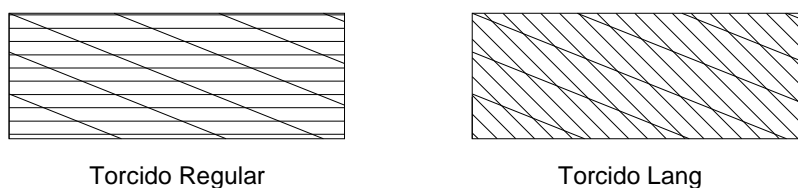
Tipos de fabricación de cables de acero. ⁶
